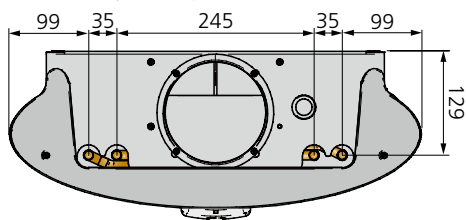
Dimensions ADRIATIC AWC Ellips, vue arrière du raccordement hydraulique
